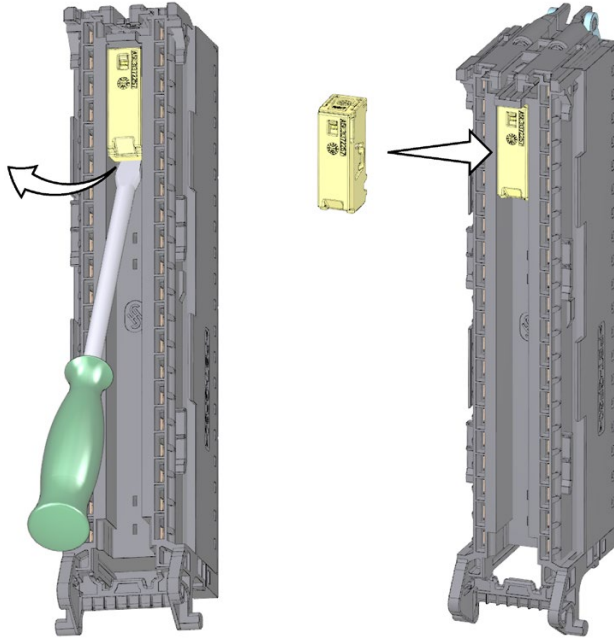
Elektronisches Kodierelement aus Frontstecker entfernen und in neuen Frontstecker einsetzen
